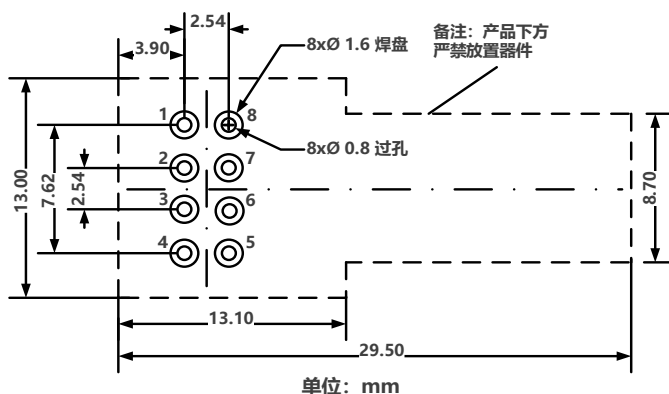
PCB Layout 设计推荐尺寸图 (俯视图)
